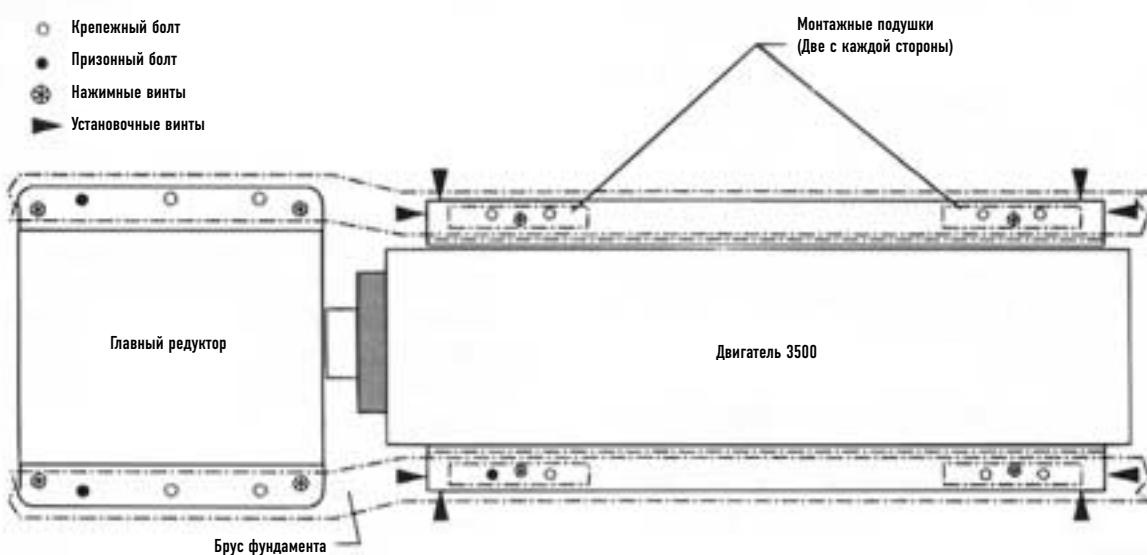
План фундамента под отдельно монтируемый редуктор/двигатель
